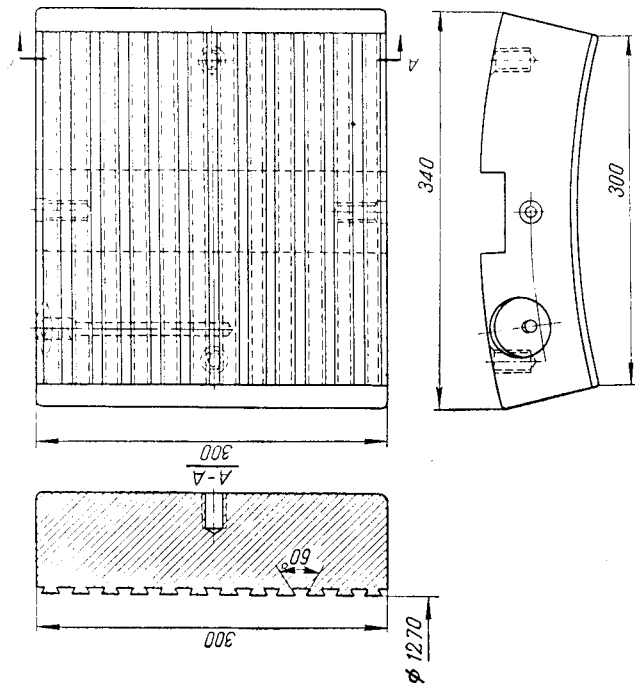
Сегмент направляющего подшипника, обработанный под заливку баббитом
